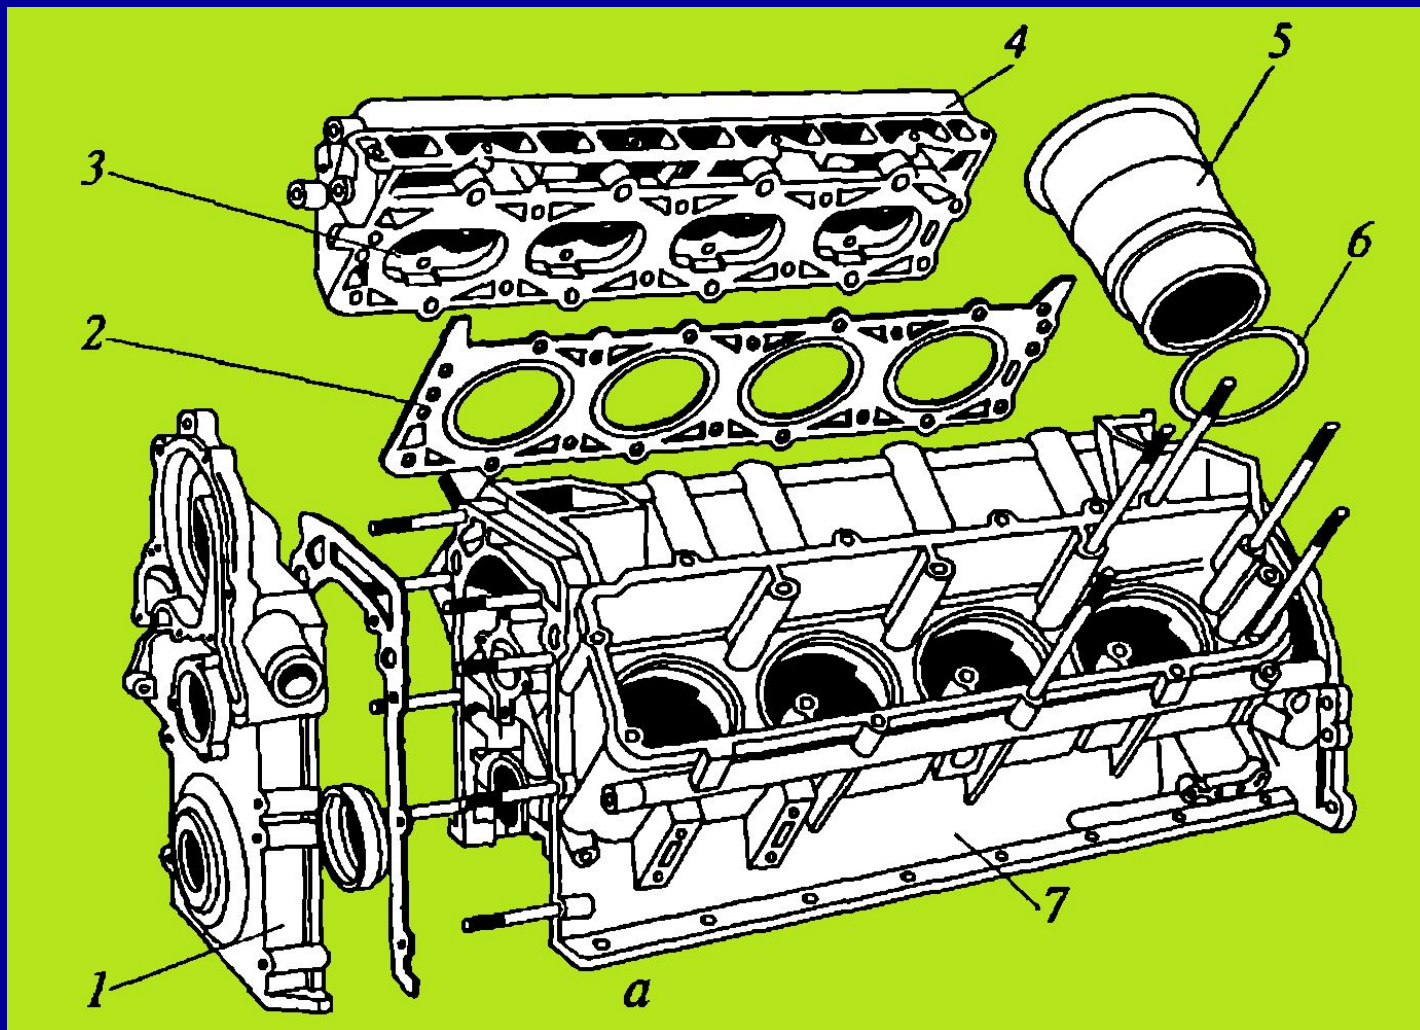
а. Детали кривошипно-шатунного механизма V-образного карбюраторного двигателя;
